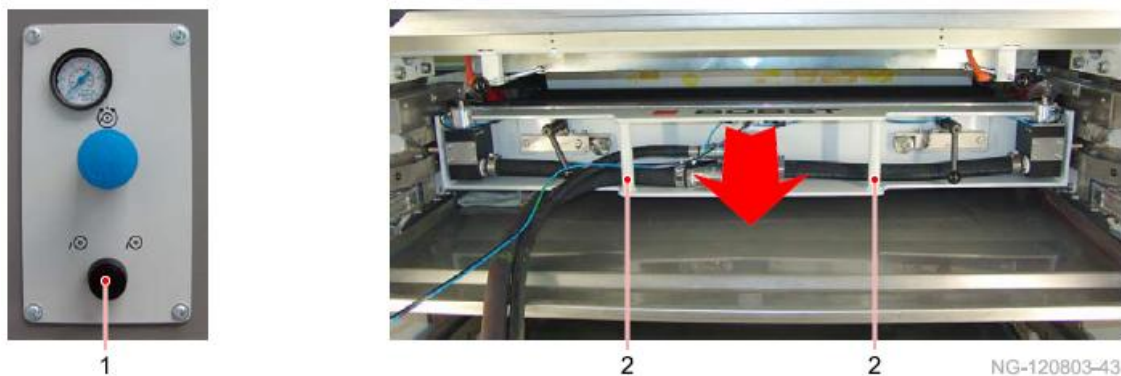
Desmontaje y limpieza de rasqueta (1/4).
